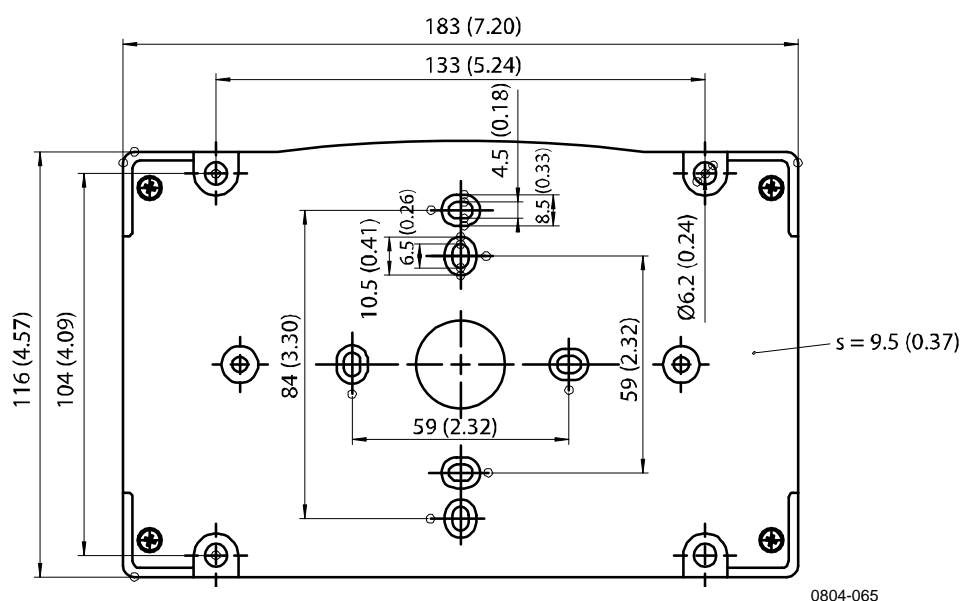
Dimensions de la plaque de montage plastique (mm/pouce)
